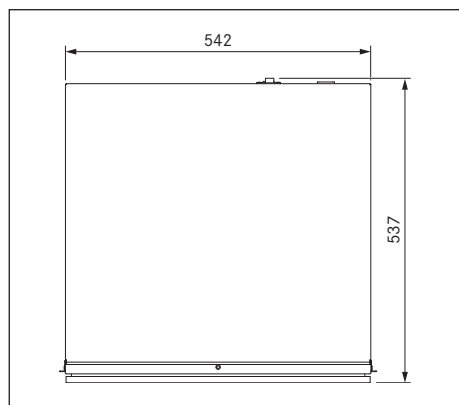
Dimensões do aparelho MS290, vista de cima
